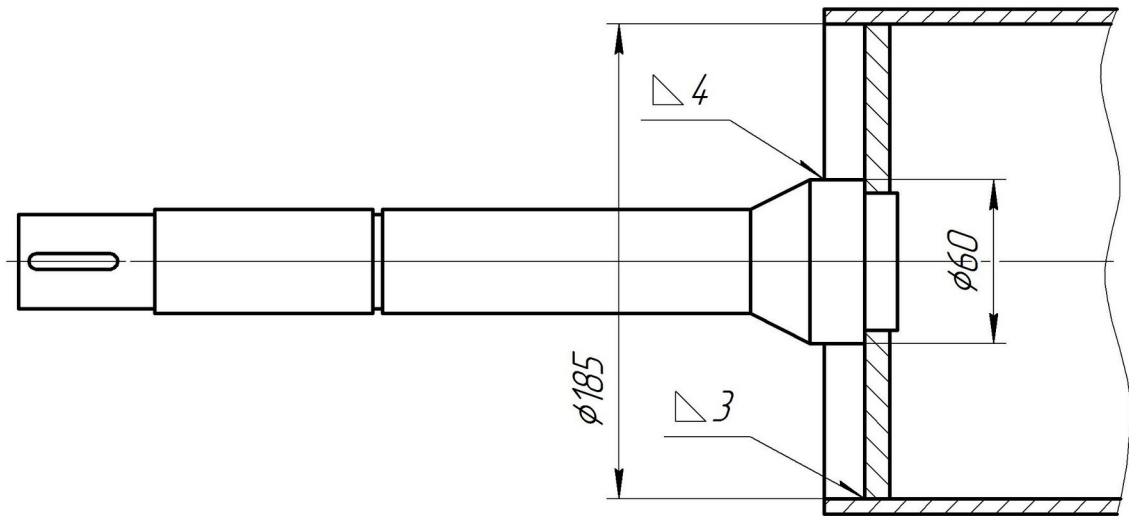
Схема приварки цапфи вала очищувально-передавального вальця
